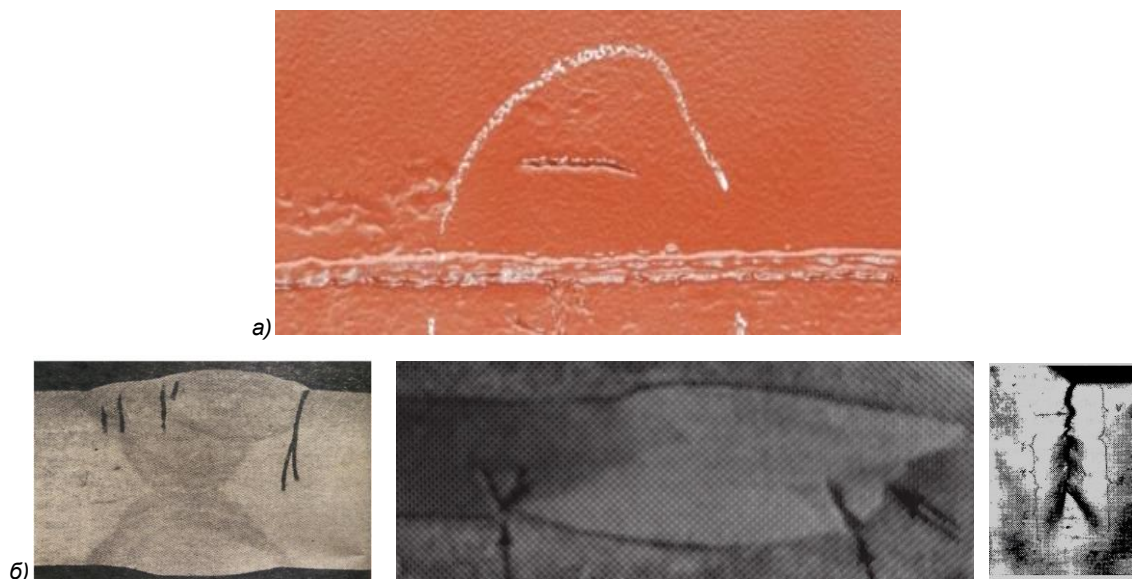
Трещина в наружной обшивке т/х «Ладoga», развивающаяся при поперечной нагрузке вне области ЗТВ (а), и трещины в сварном шве и ЗТВ (б) в соединениях корпусных конструкций и трубопроводов [7, 8]
